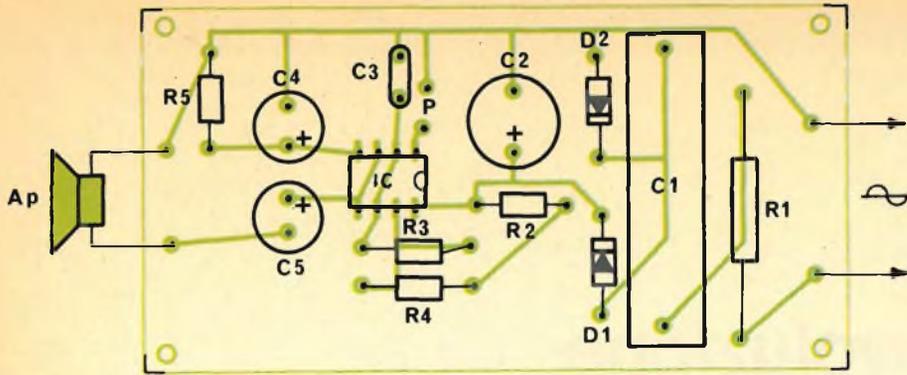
/a - Disposizione dei componenti sulla basetta del campanello.
